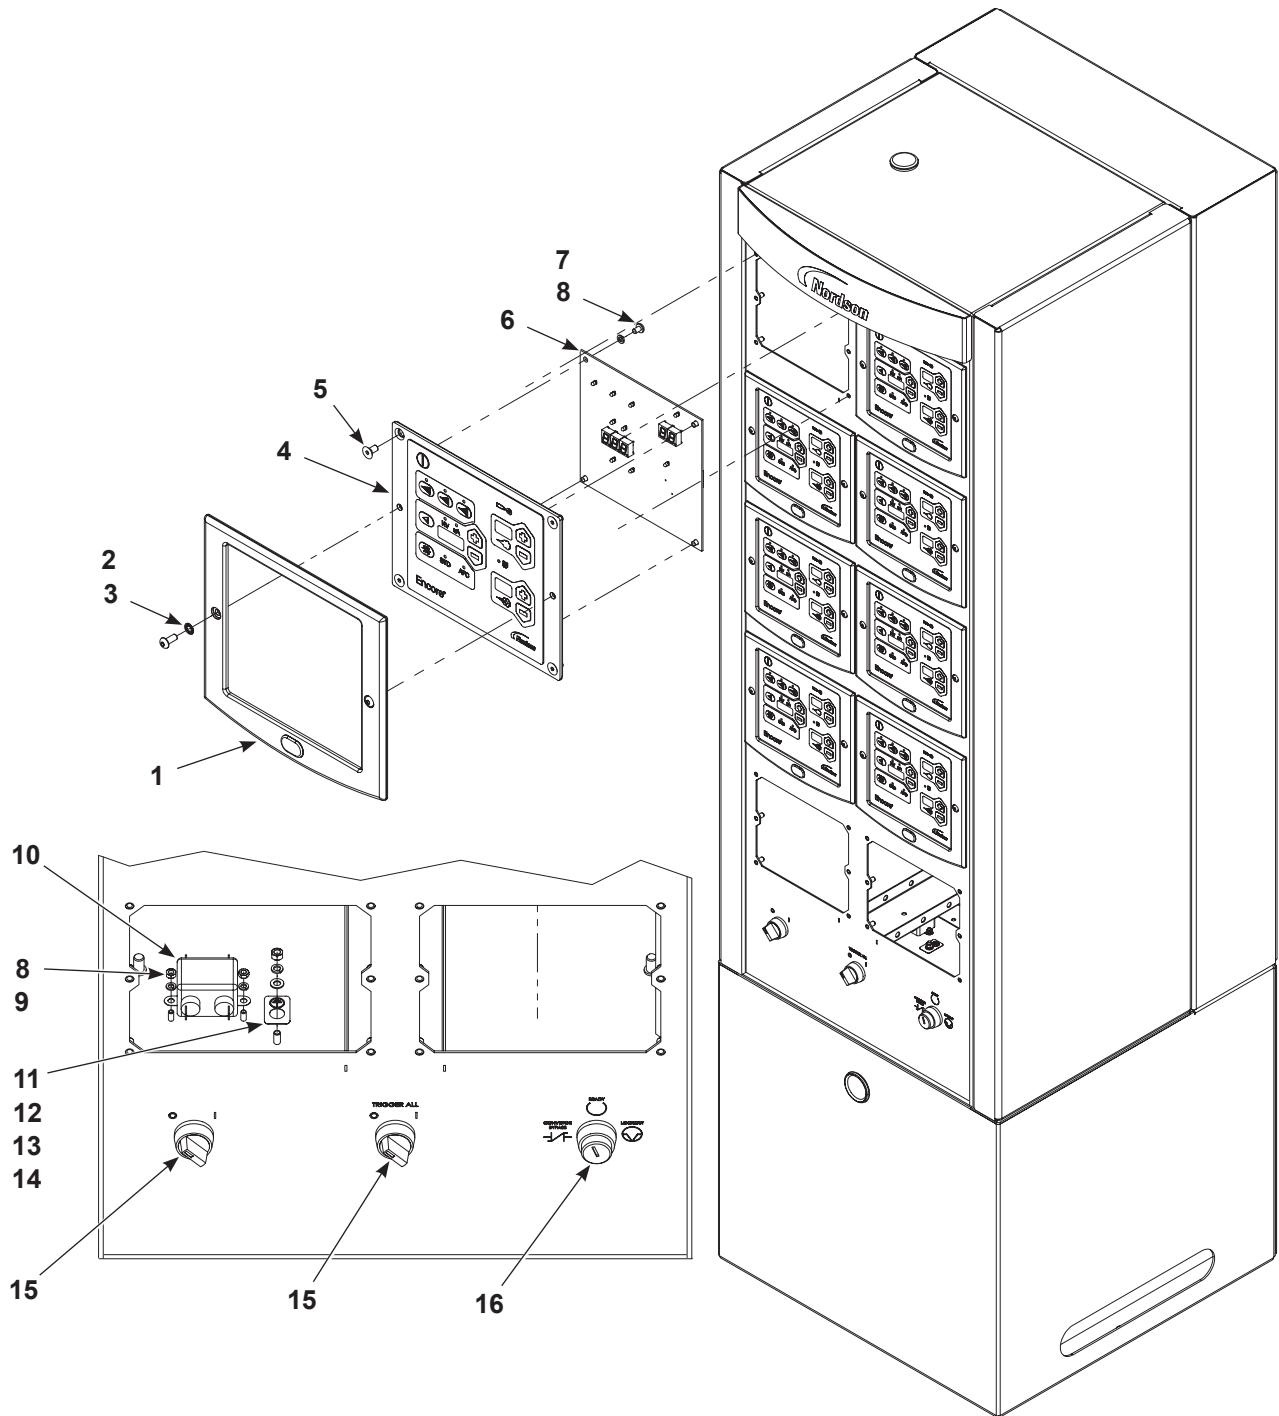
Piezas del panel frontal para controlador de pistolas múltiples
